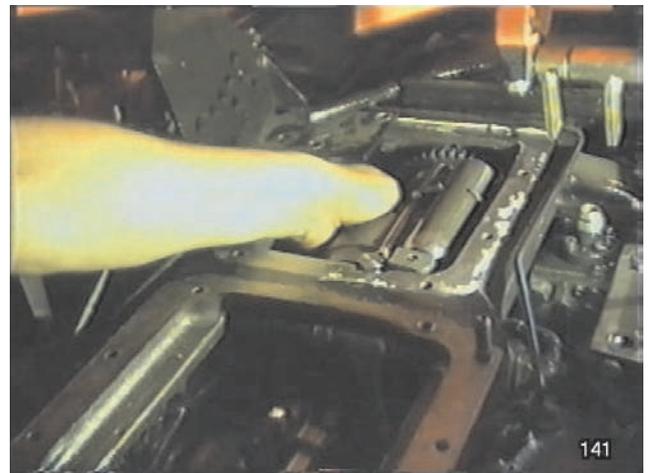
Déposer le relevage et le couvercle avant du carter de boîte arrière et accéder à l'ensemble de l'embrayage de la P.d.F..
